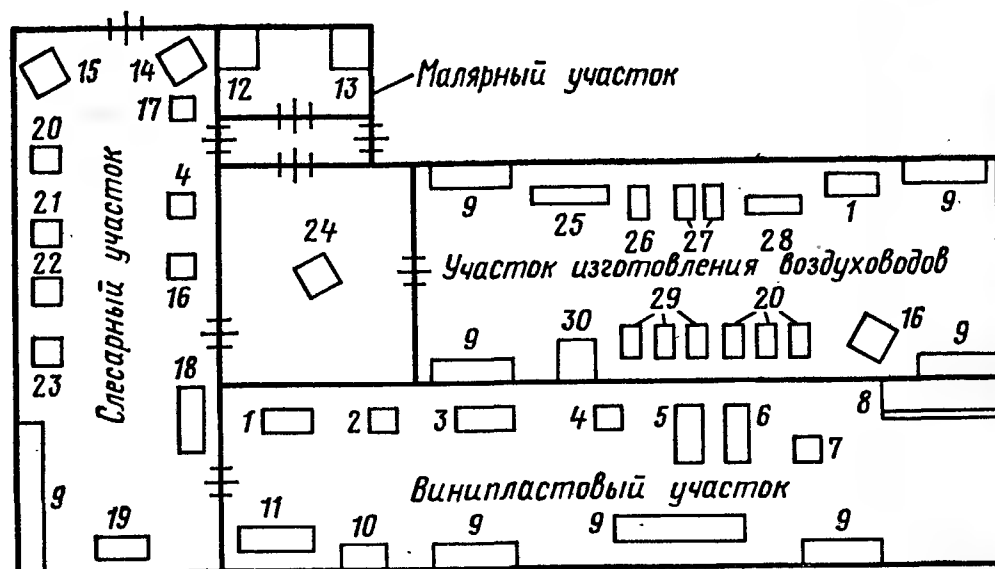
Механизированный заготовительный участок изготовления воздуховодов.
